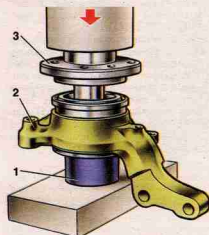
Запрессовка ступицы колеса: 1 – оправка; 2 – поворотный кулак; 3 – ступица
